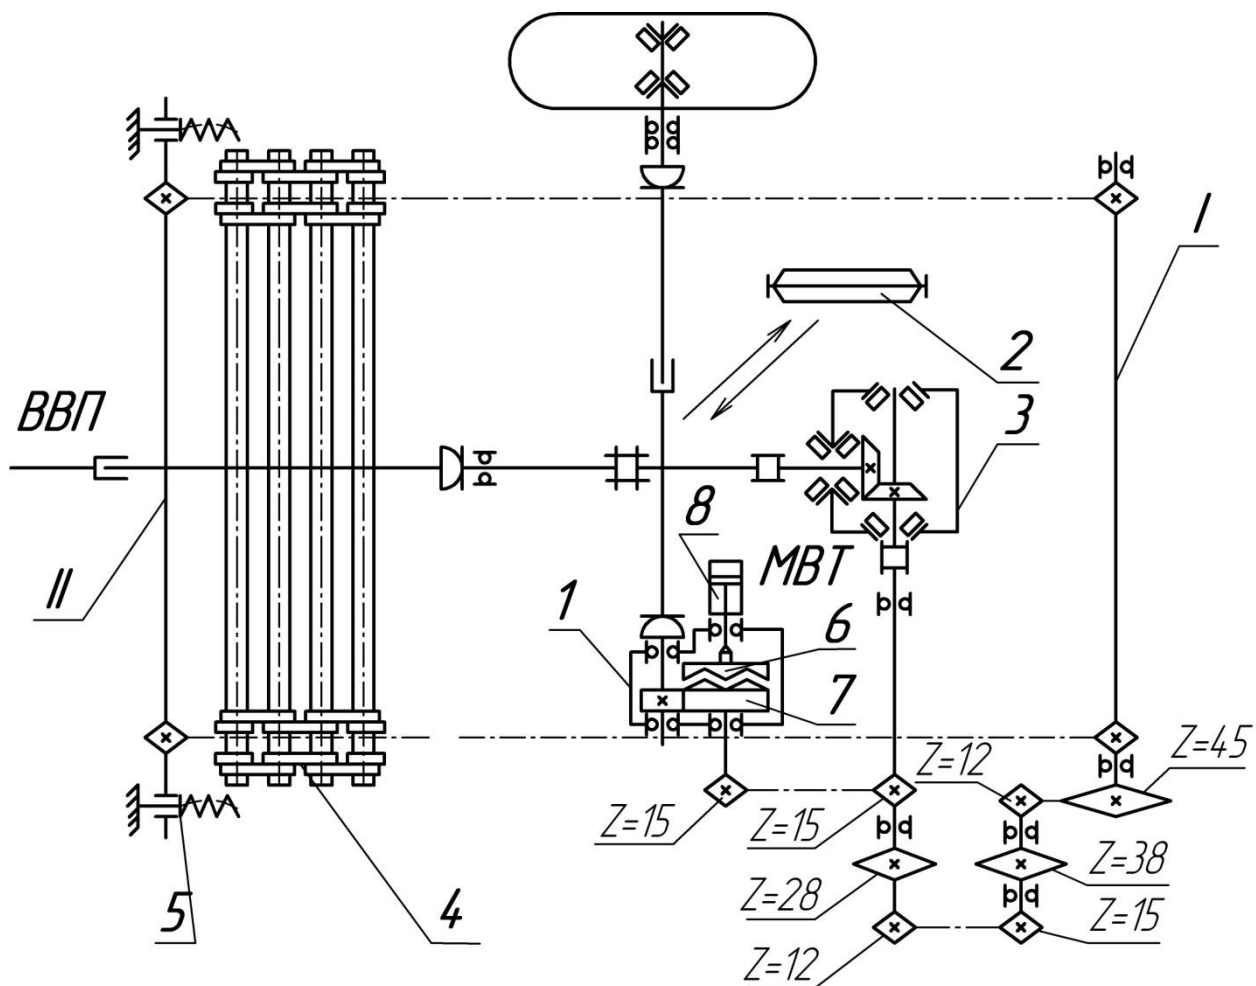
Кінематична схема механізму привода транспортера: I – ведучий вал транспортера; II – ведений вал транспортера; МВТ – механізм включення муфт; 1 – редуктор механізму привода транспортера від опорного колеса; 2 – блок змінних муфт; 3 – редуктор; 4 – транспортер; 5 – натяжний пристрій транспортера; 6 – напівмуфта; 7 – зубчате колесо; 8 – гідроциліндр
